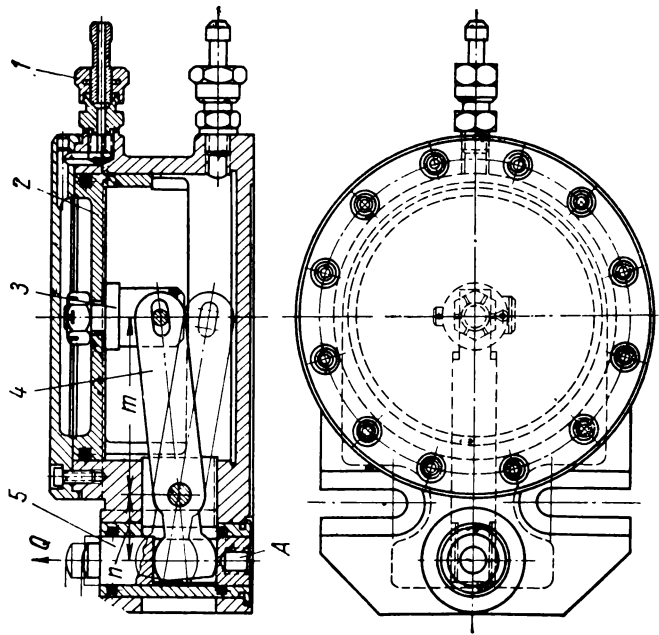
Отделенный поршневой пневматический привод с рычагом
